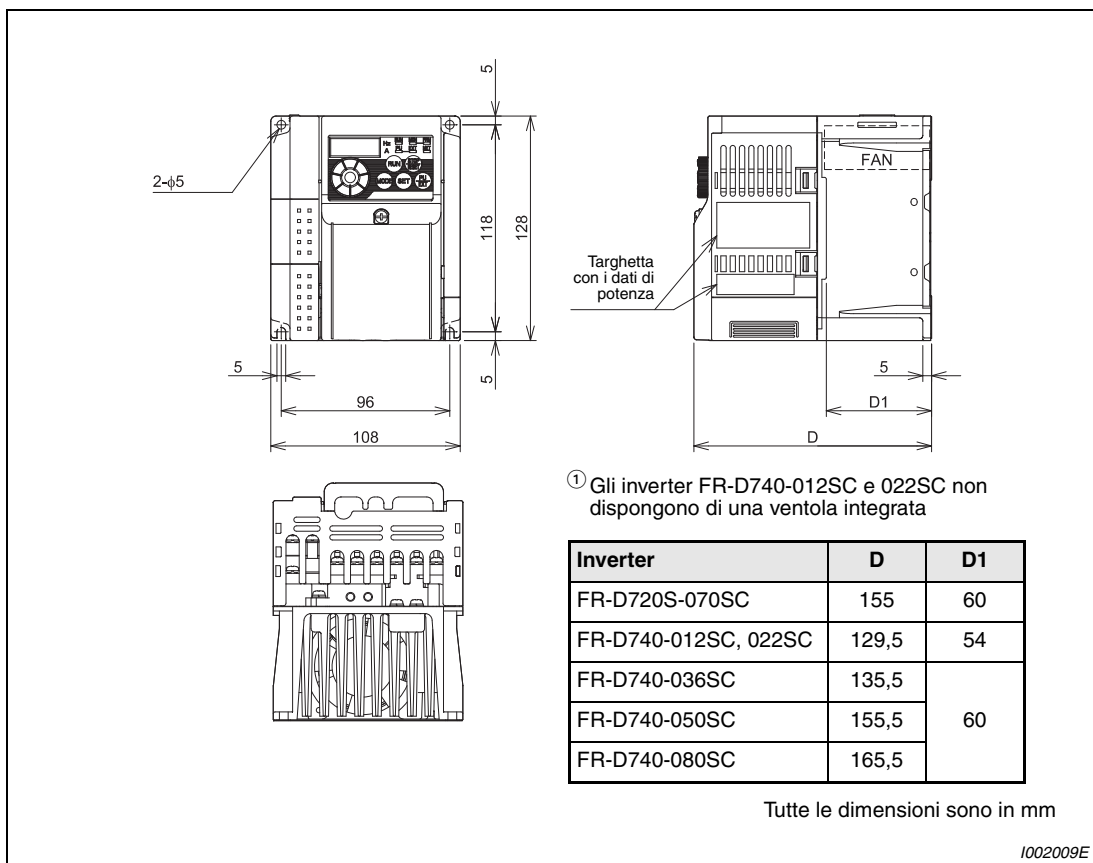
Dimensioni degli inverter FR-D720S-070SC e da FR-D740-012SC a 080SC
